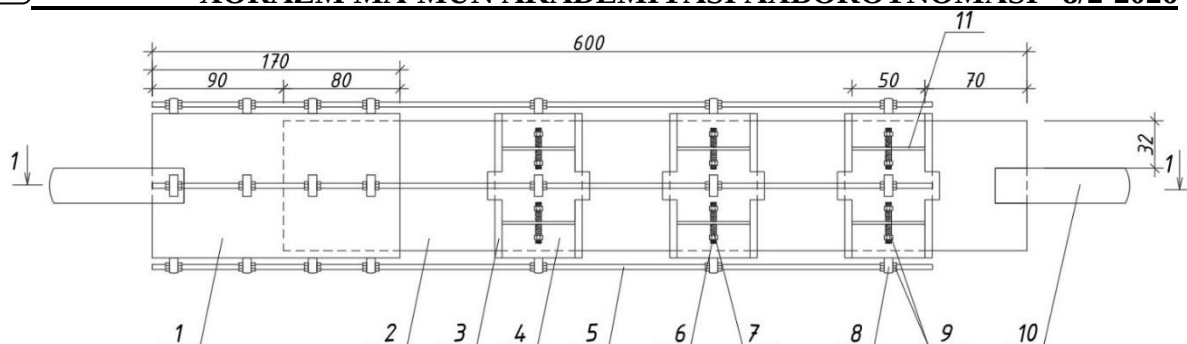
Общий вид фрикционного демпферного устройства: 1 - внешний профиль; 2 - внутренний профиль; 3 - пластический материал; 4 - обойма; 5 - стальной винт; 6 - резьбовой винт; 7 - упругие элементы; 8 - крепления; 9 - гайки; 10 - опорная часть демпфера; 11 - соединительная деталь обоймы; 12 - сварное соединение; 13 - ограничитель прокладки
